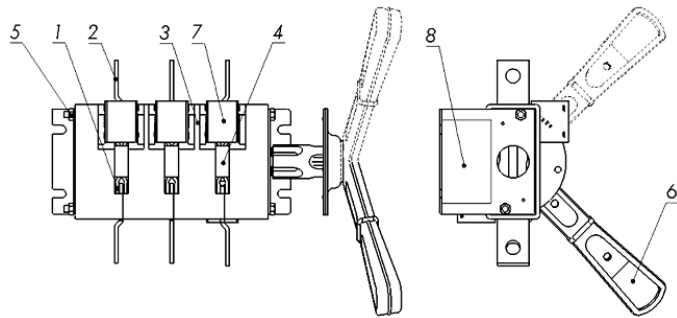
Общий вид трехполюсного выключателя-разъединителя на одно направление со вспомогательными контактами
